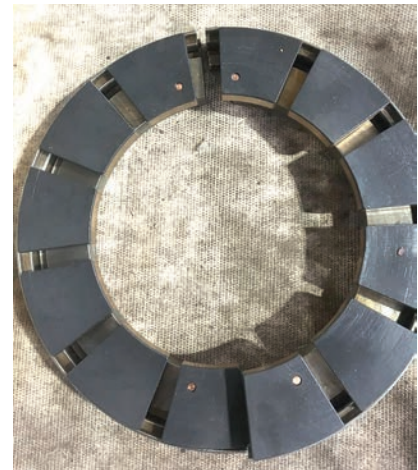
Колодки опорно-упорного подшипника ротора осевого компрессора турбины высокого давления после 3016 ч эксплуатации
